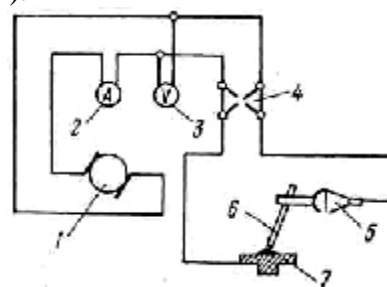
Схема установки дуговой сварки постоянным током:
